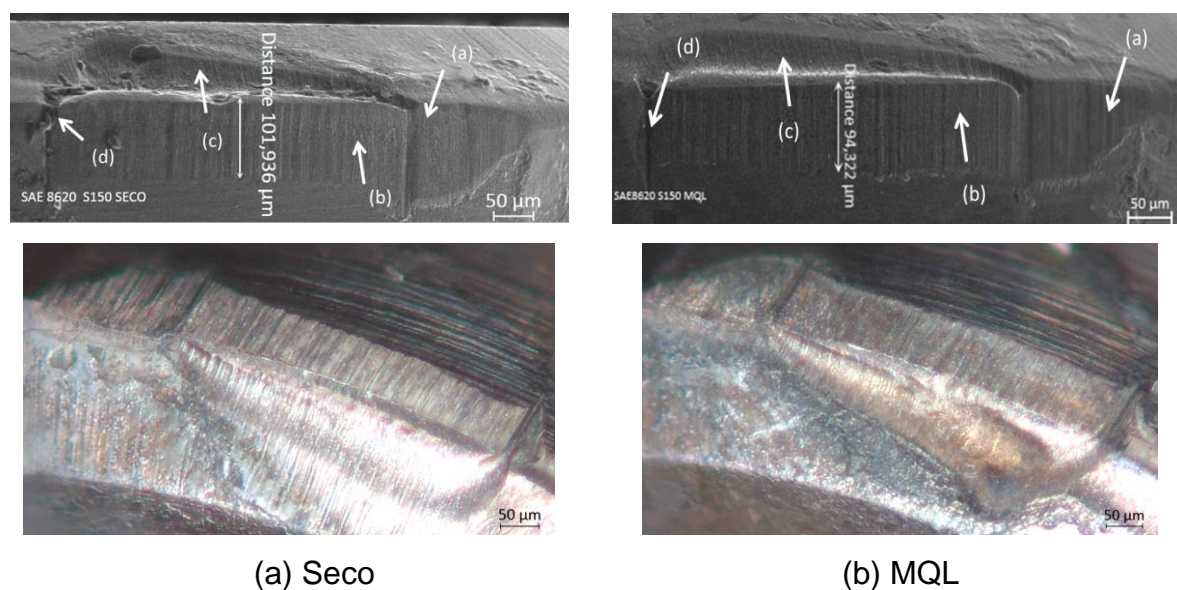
Desgaste de flanco SAE 8620 MQL e seco, $V_c=150$ m/min. Fonte própria.
